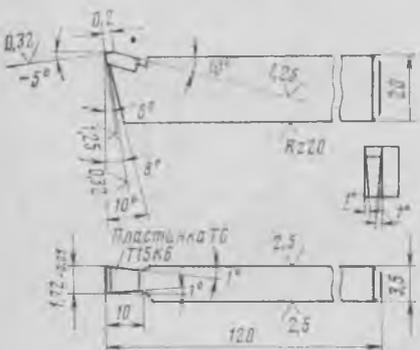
Резец канавочный для прорезки канавок в роторе 3404.06.001.1
